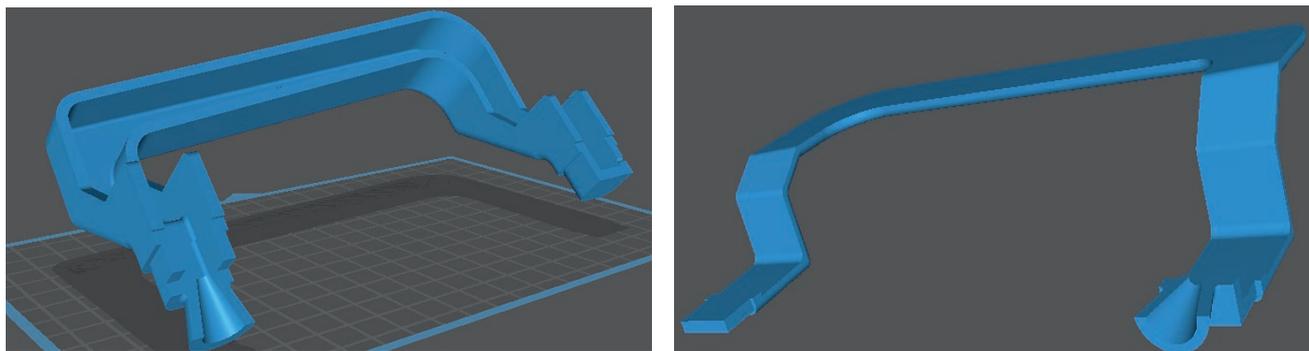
Части пресс-формы для отливки «Ручка»: *а, б* – нижняя и верхняя полуформы
